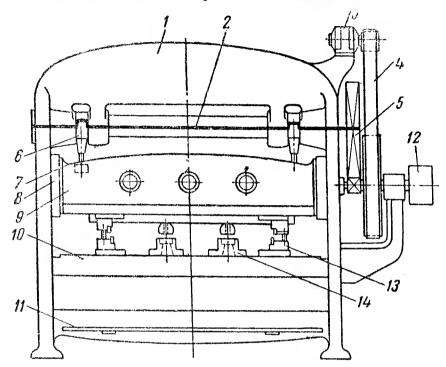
Схема кривошипного двухступенчатого пресса. 1 — станина; 2 — коленчатый вал; 3 — электродвигатель; 4 — ременная передача; 5 — шестеренчатая передача; 6 — шатун; 7 — устройство для регулировки высоты ползуна; 8 — направляющие; 9 — подвижной стол (ползун); 10 — стол неподвижный; 11 — педаль; 12 — муфта включения; 13 — ножедержатели; 14 — штампы.
